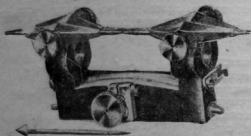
Циркуль для проверки колес с параллельными губками.
